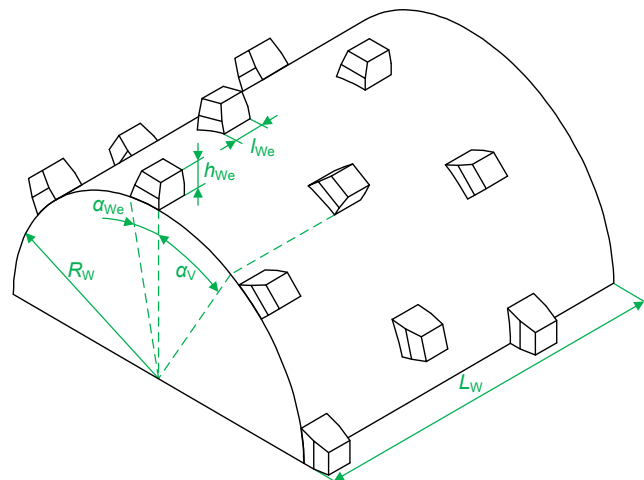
Abmessung von Grundkörper und Werkzeugen einer Walze zur Beschreibung der Werkzeugform
